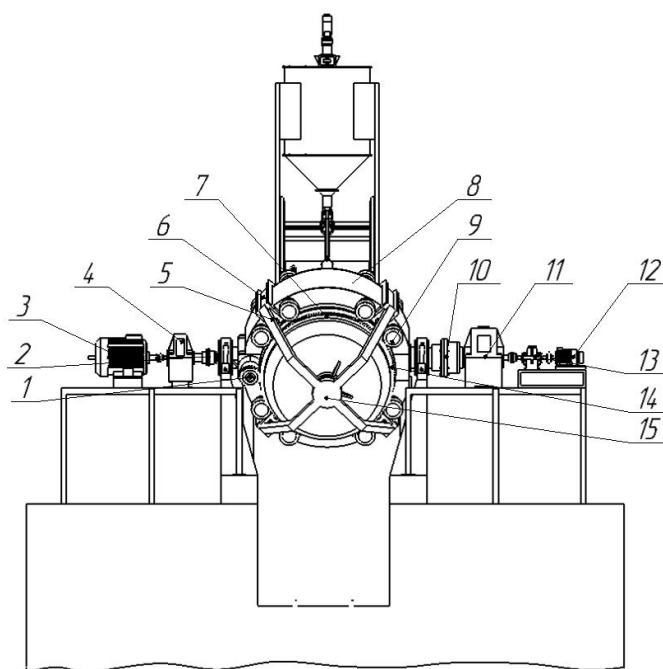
Схема компоновки механизмов наклона и поворота 10-тонного кислородного конвертера конструкции ДонНТУ
